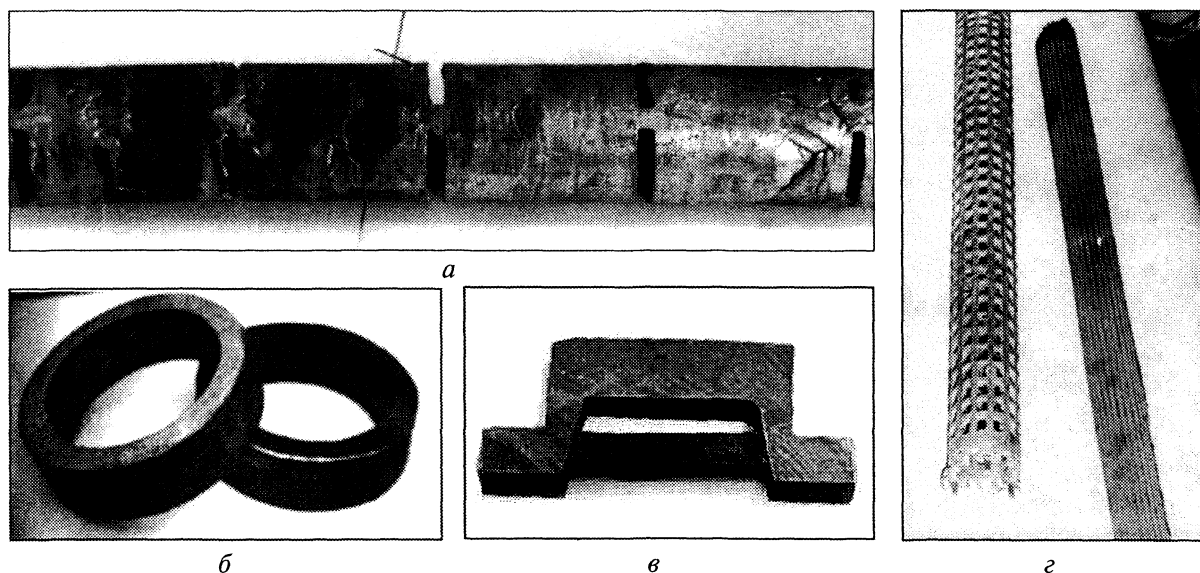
Заготовки, полученные вертикальным непрерывным литьем
